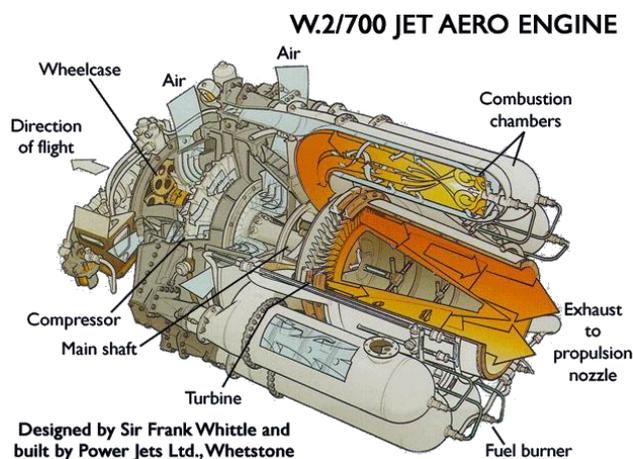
Газотурбинный двигатель Френка Уиттла
